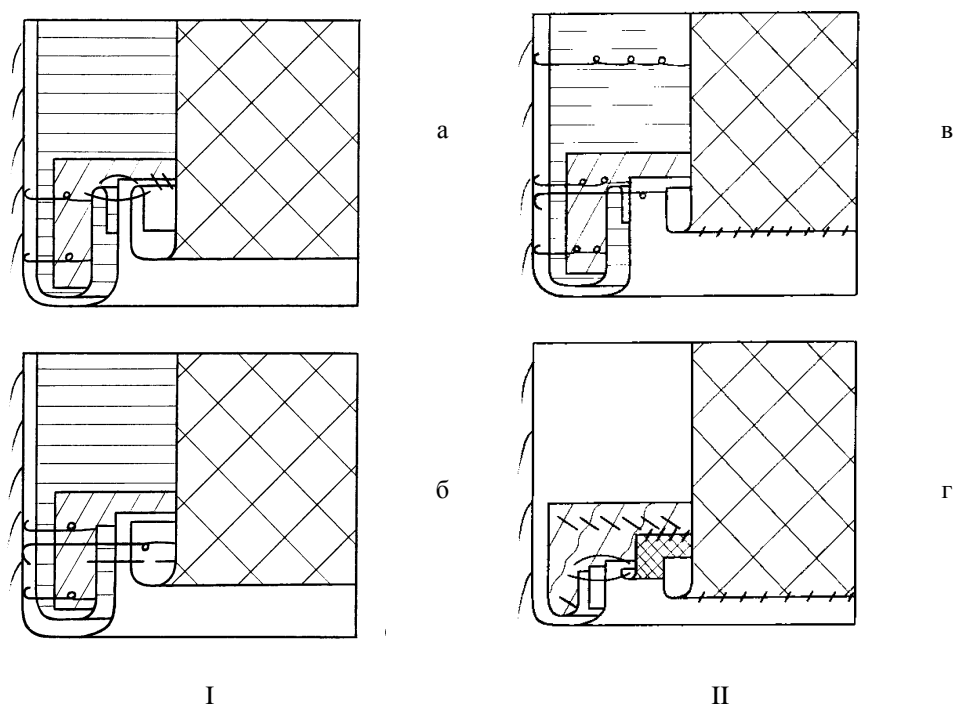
Монтажные схемы конструкций соединения рукава с подкладкой по низу рукава: I – соединение рукава с подкладкой машинным способом; II – соединение рукава с подкладкой ручным способом
